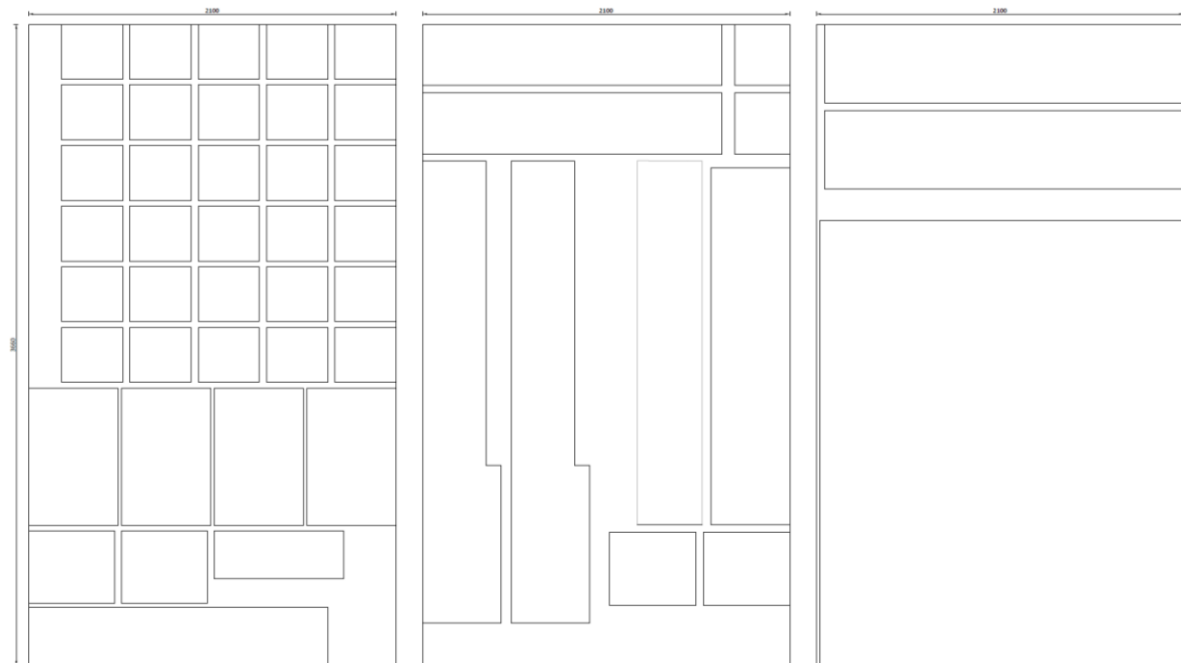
Garrafeira. Planificação de corte da Chapa.
